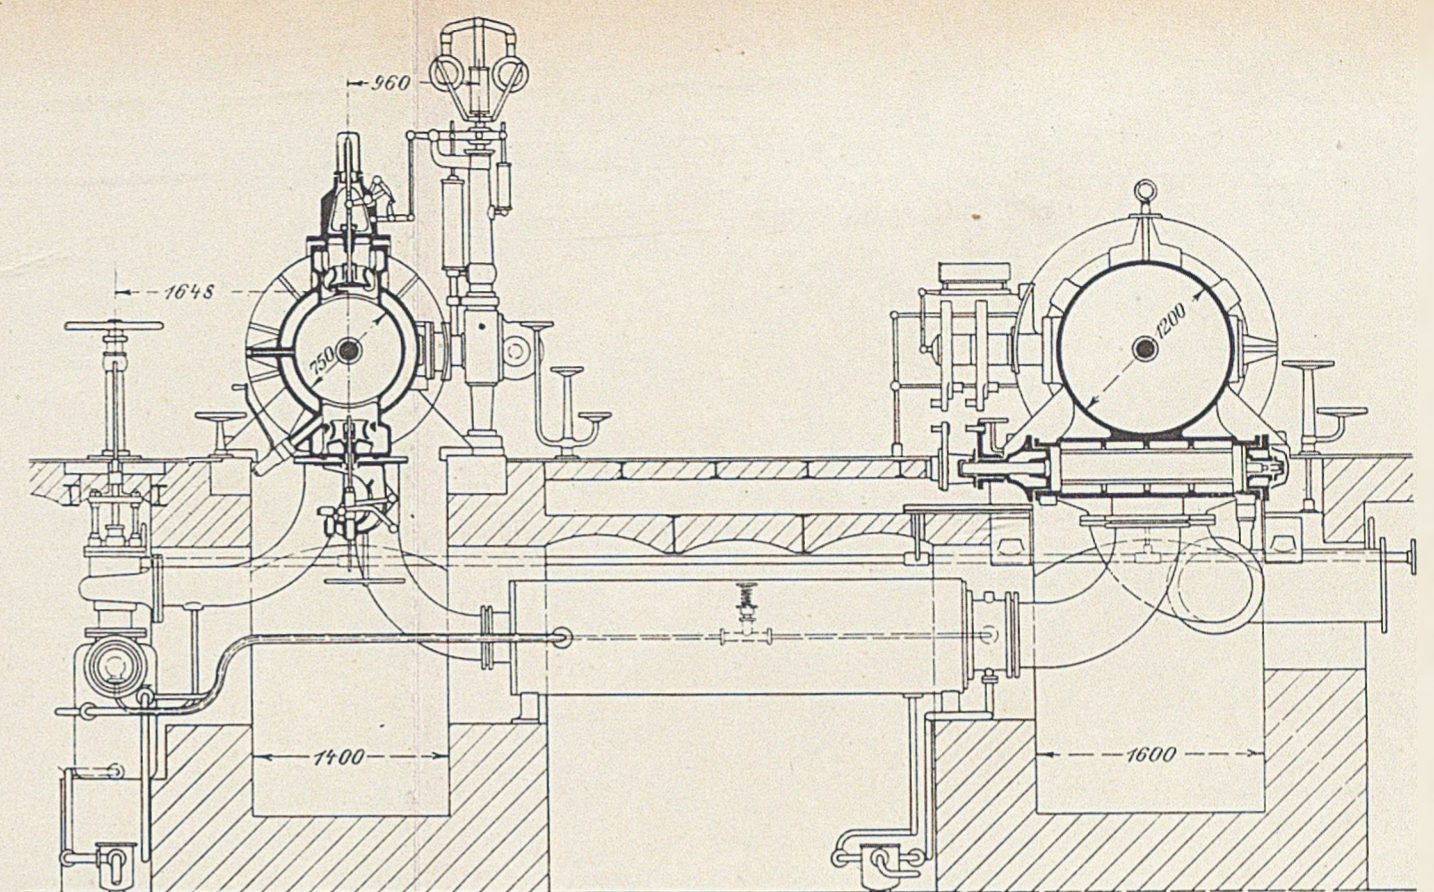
Senkrechter Querschnitt durch die Steuerung des Hoch- und Niederdruckzylinders.
